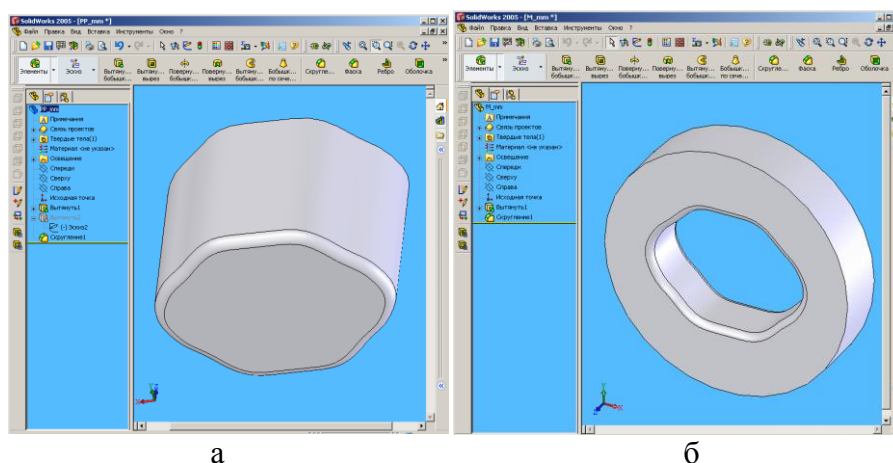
Твердотільні моделі: а – пуансона і б– матриці для першого переходу витягування коробчастого виробу.
